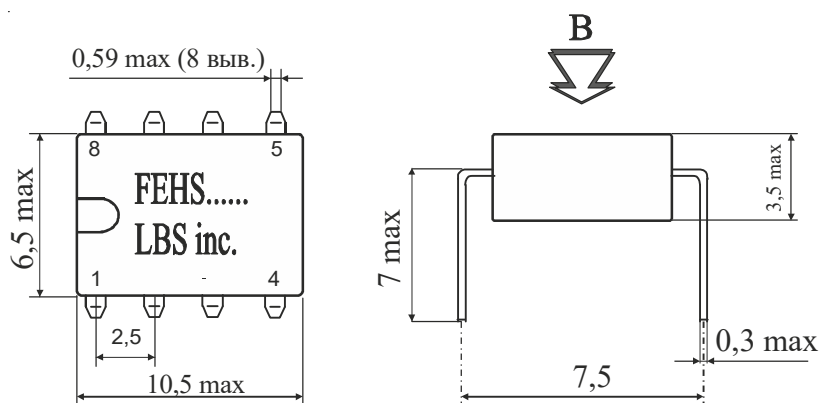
Габаритный чертеж ПДХ в корпусе DIP-8 (2101.8-1).
